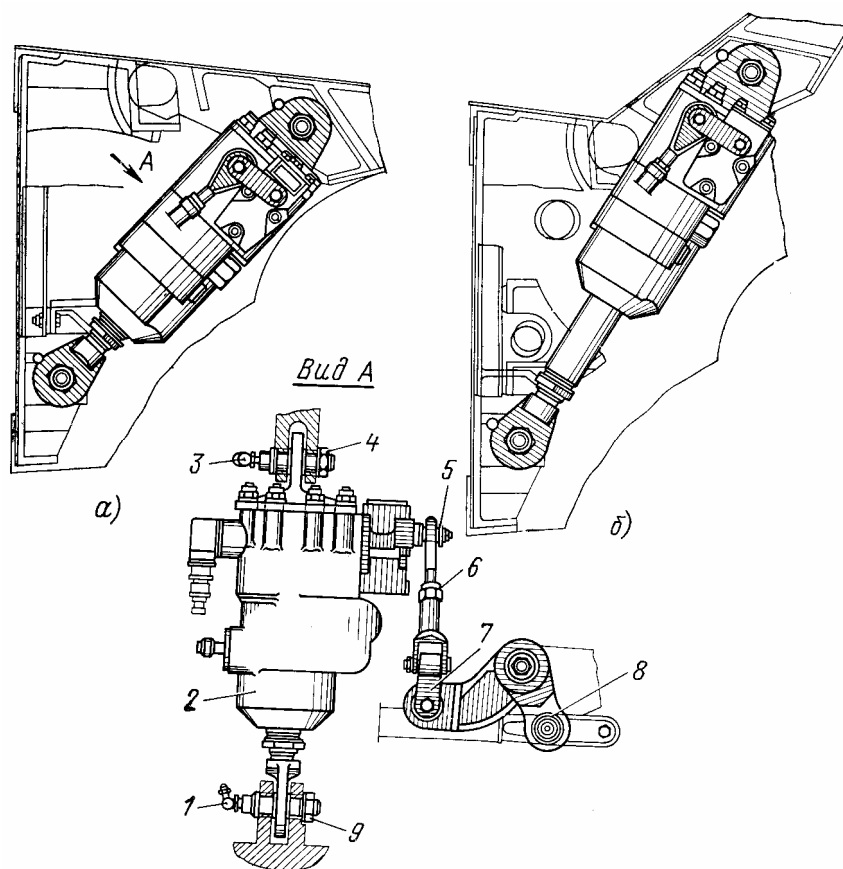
Установка рулевого привода РП-59 (на правом крыле, нервюра 16):
